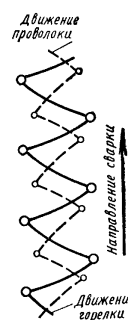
Движение горелки и присадочной проволоки при сварке угловых швов
